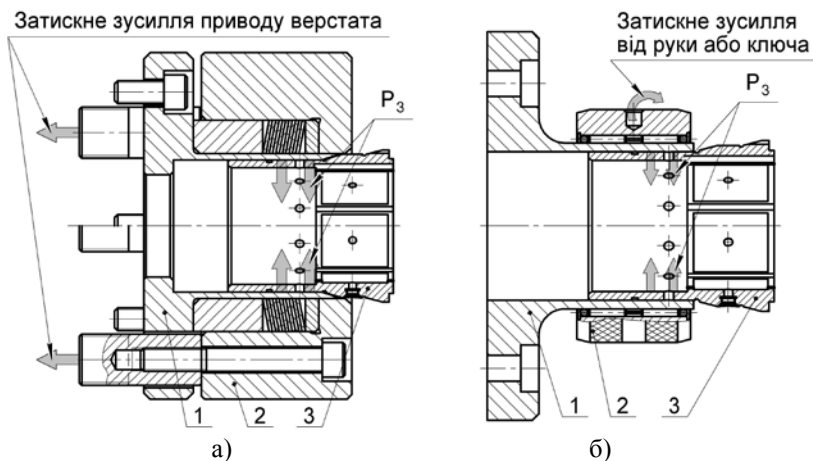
Загальний вид схем закріплення гідростатичної втулки в патроні з тарілчастими пружинами а) та в роликовому патроні б): 1 – корпус, 2 – обойма, 3 – гідростатична втулка
